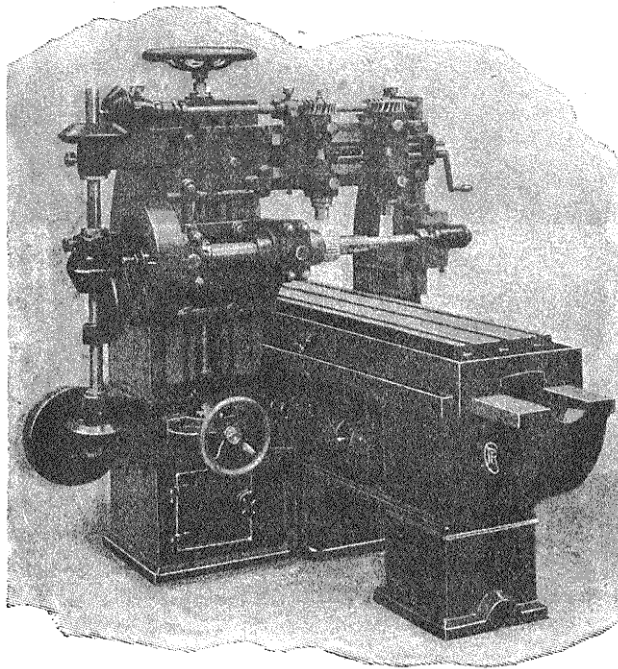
Machine à fraiser longitudinale Reinecker.
